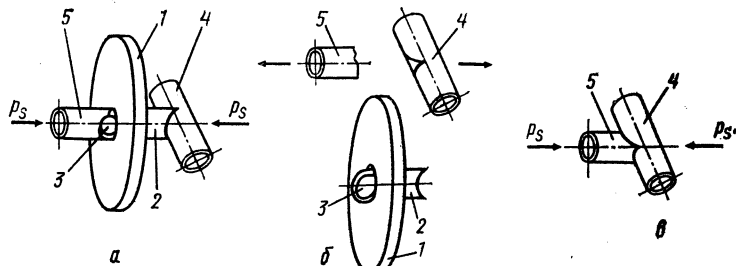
Принцип сварки разветвлений труб в выточку: а — подогрев свариваемых труб; б — отвод нагретого инструмента; в — состыковка (сварка); 1 — нагретый инструмент; 2 — сварочный инструмент для выравнивания кольцеобразной выточки в трубе с  $D_{\text{усл}}$  большего размера; 3 — сварочный инструмент для разветвляемой трубы с  $D_{\text{усл}}$  меньшего размера; 4 — труба с  $D_{\text{усл}}$  большего размера; 5 — труба с условным проходом меньшего размера
